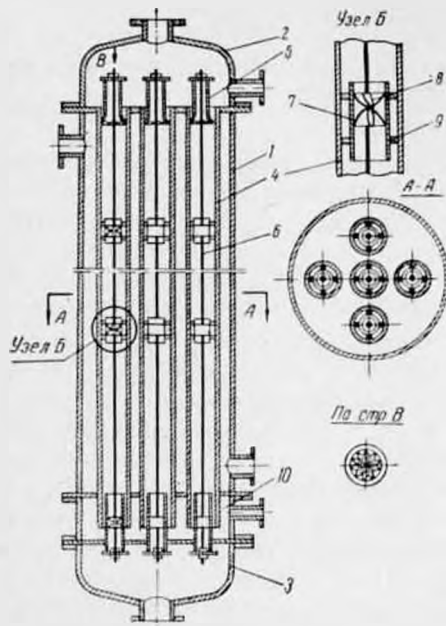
Конструкция кожухотрубного противоточного аппарата: 1—корпус, 2—верхняя и 3—нижняя камеры, 4—контактные трубки, 5—насадки жидкой фазы, 6—стержень, 7—цилиндрические стаканы, 8—статические закручиватели, 9—дистанционные выступы, 10—промежуточная камера.
